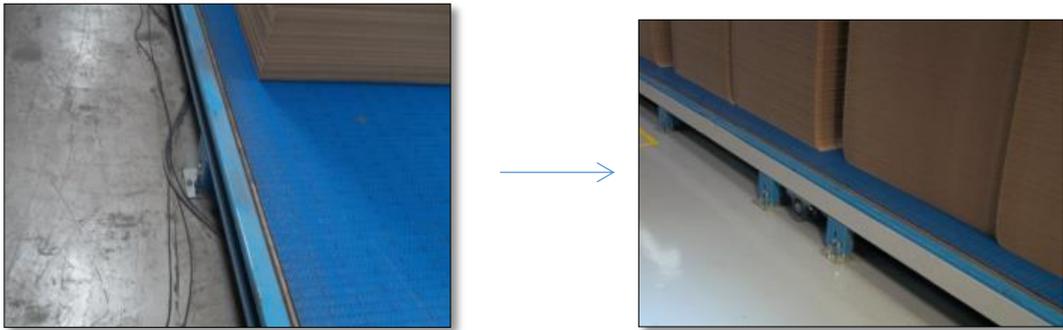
ANTES Y DESPUÉS ROSILLO.
